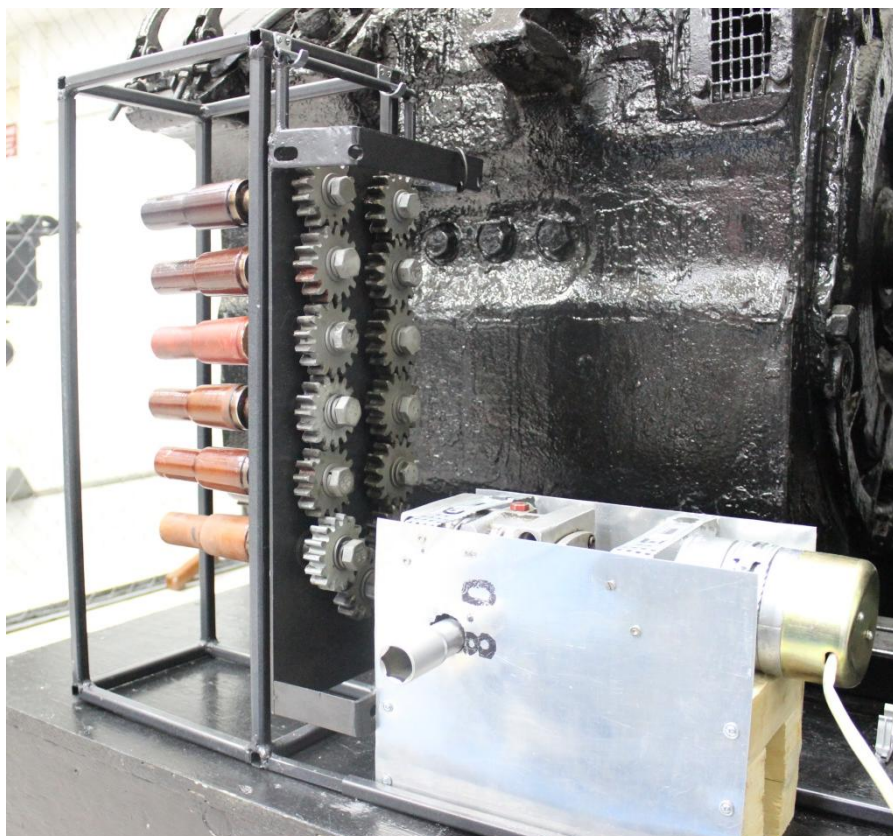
Опытный образец установки для сушки изоляционных пальцев кронштейнов щёткодержателей
